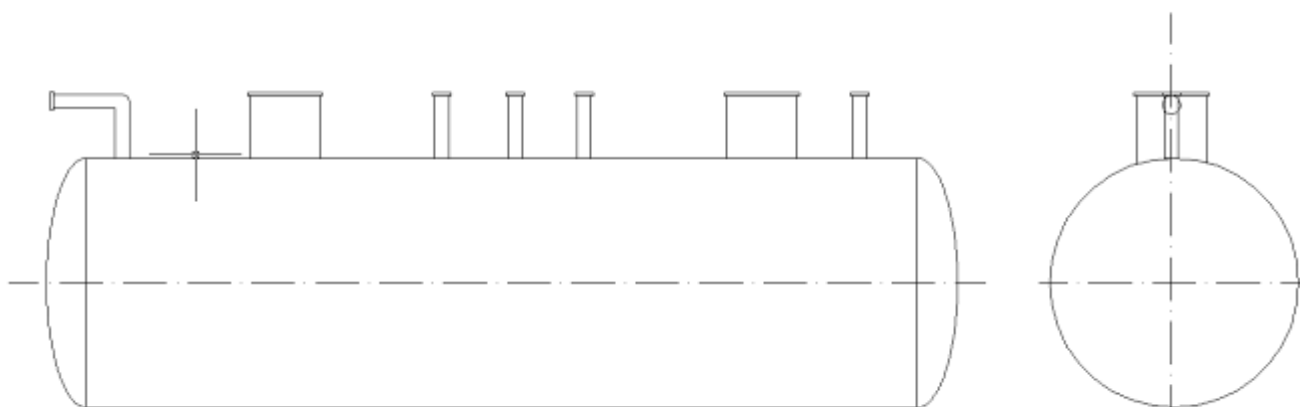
Эскиз общего вида резервуара РГС-60
